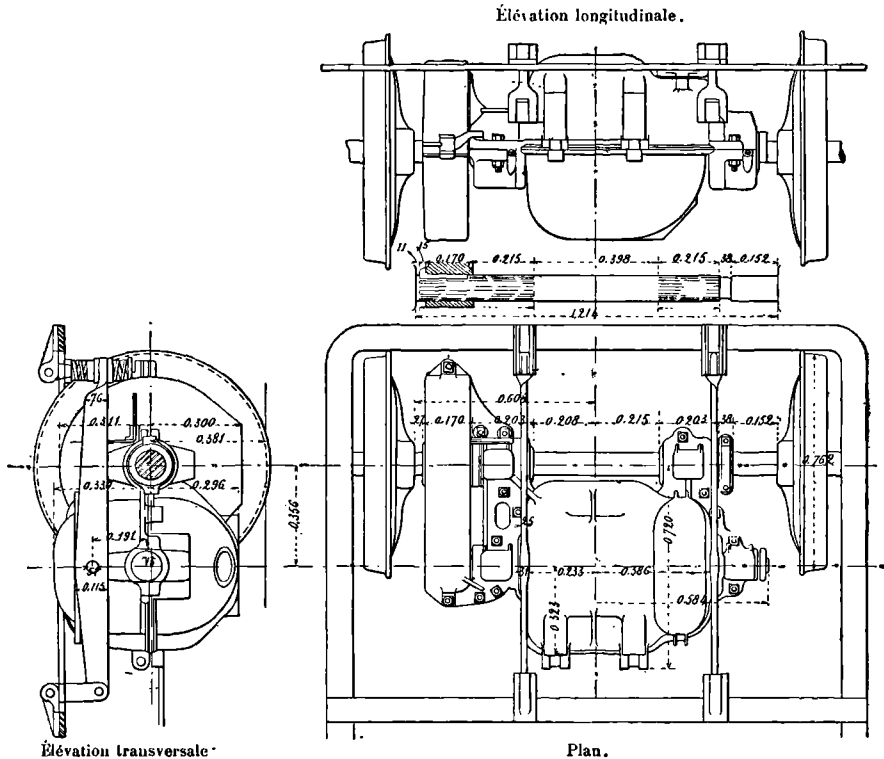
Dessins d'encombrement du moteur G. E. 1000, suspendu par barres latérales.
